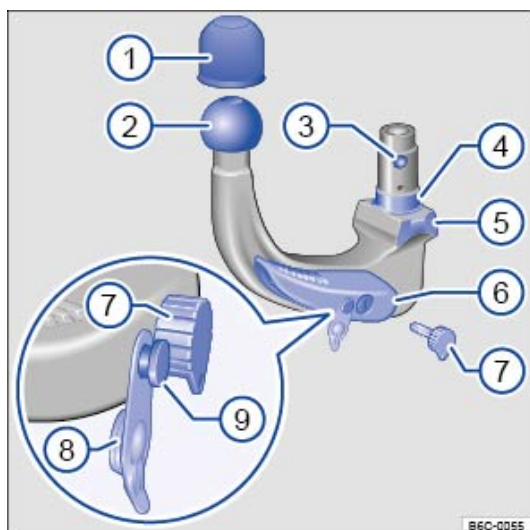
Vue d'ensemble : boule amovible du dispositif d'attelage
